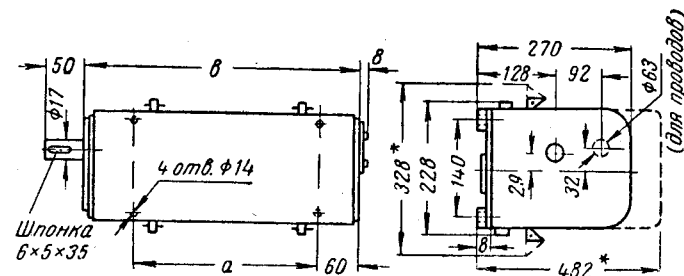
Командоаппараты КА-4024, КА-4044 и КА-4054 (без редуктора)\*; габаритные размеры с открытыми замками и снятым кожухом.
